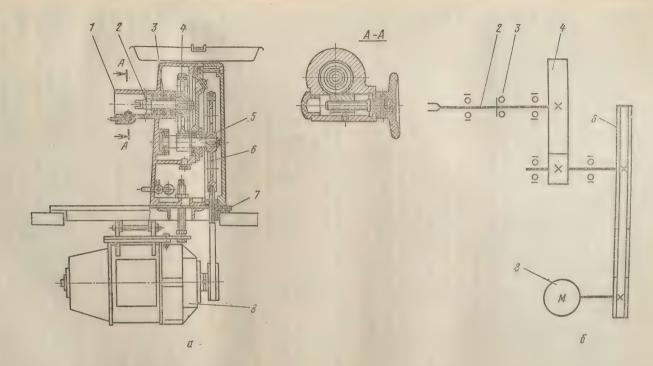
Привод ПУВР-0,4: a — общий вид;  $\delta$  — кинематическая схема
